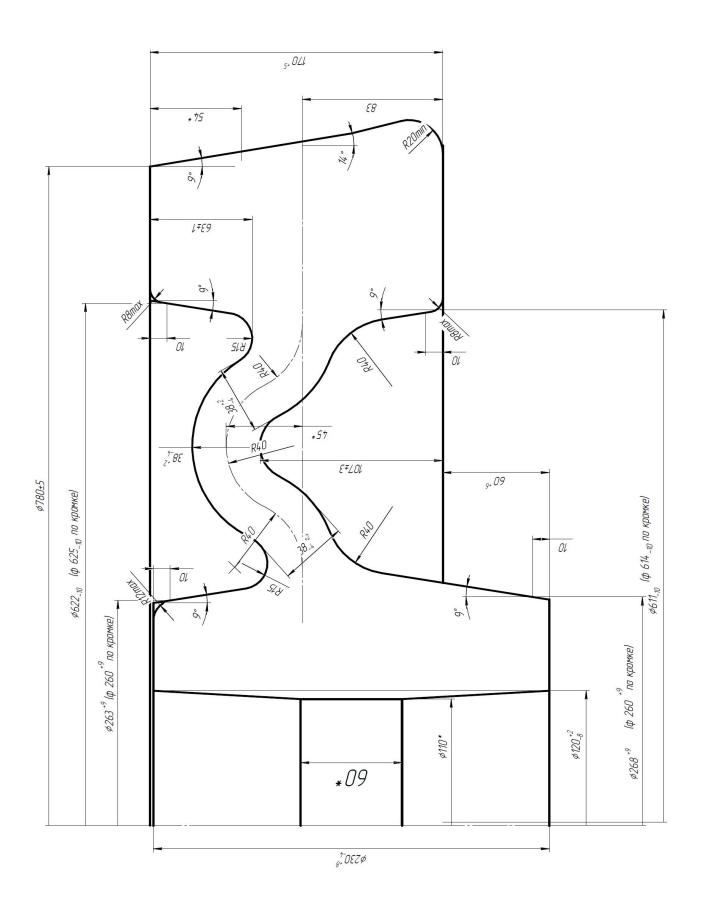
Колесо черновое Ø 780 мм по(д Ø 750 мм черт. № 29240,ред. Е). Масса чернового колеса, рассчитанная на $^2/_3$ поля допуска = 501 кг.
